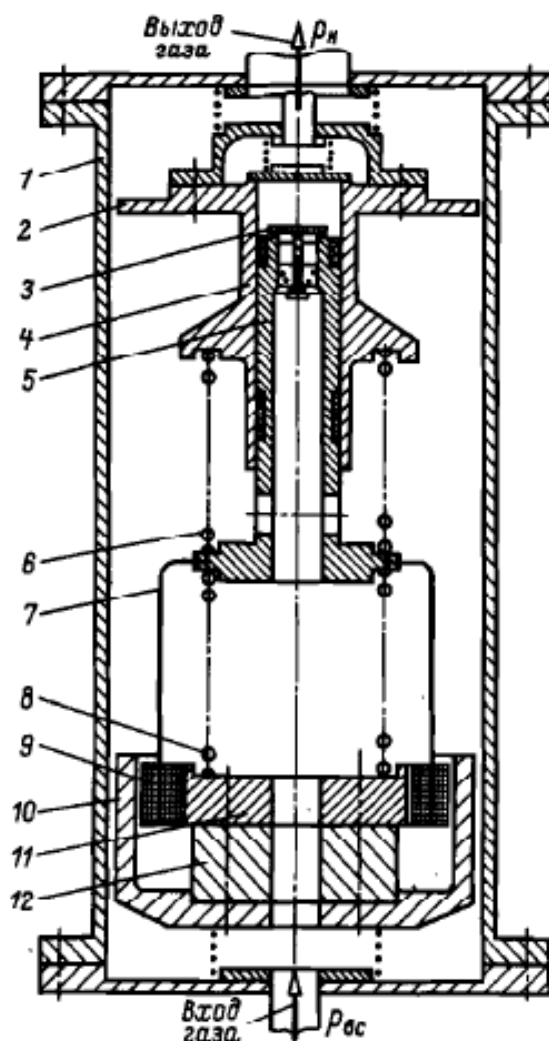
Схема магнитоэлектрического поршневого компрессора: 1- корпус; 2 – нагнетательный клапан; 3 – всасывающий клапан; 4 – цилиндр; 5 – поршень; 6 – 8 – силовые пружины; 7 – крепление катушки; 9 – катушка электромагнита; 10 и 11 – полюсные наконечники; 12 – постоянный магнит
